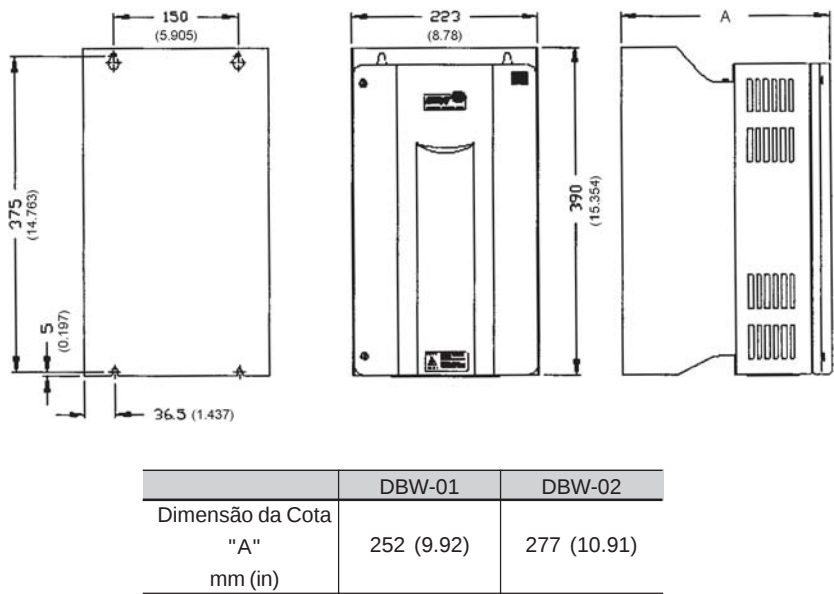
Dimensional para DBW-01 e DBW-02
